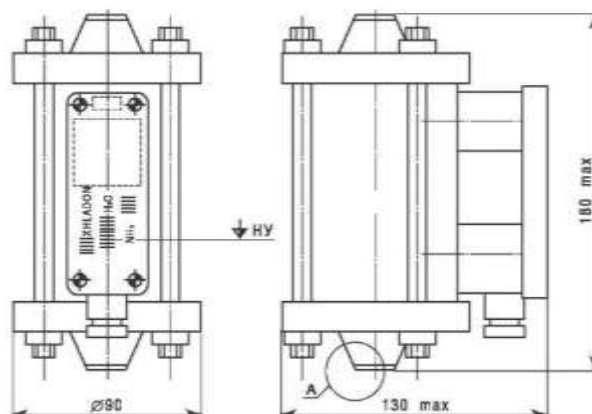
Габаритные и установочные размеры передающего преобразователя
